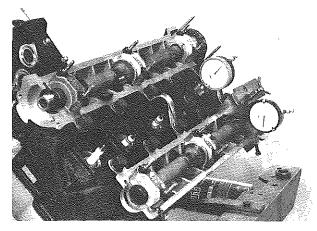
Montare il comparatore n. 42 Fit gauge No. 42
